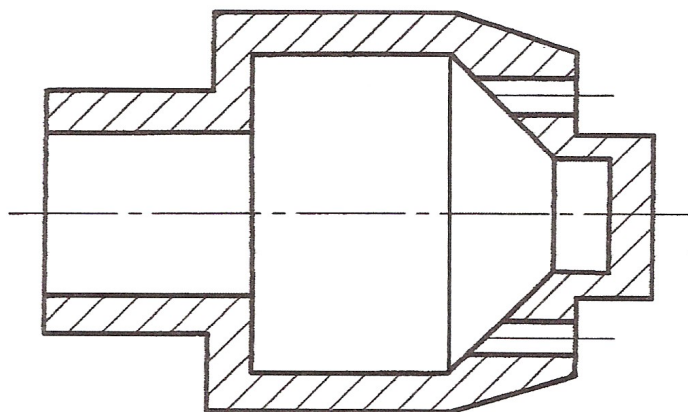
Схема конструкции сопла с разделением потока
